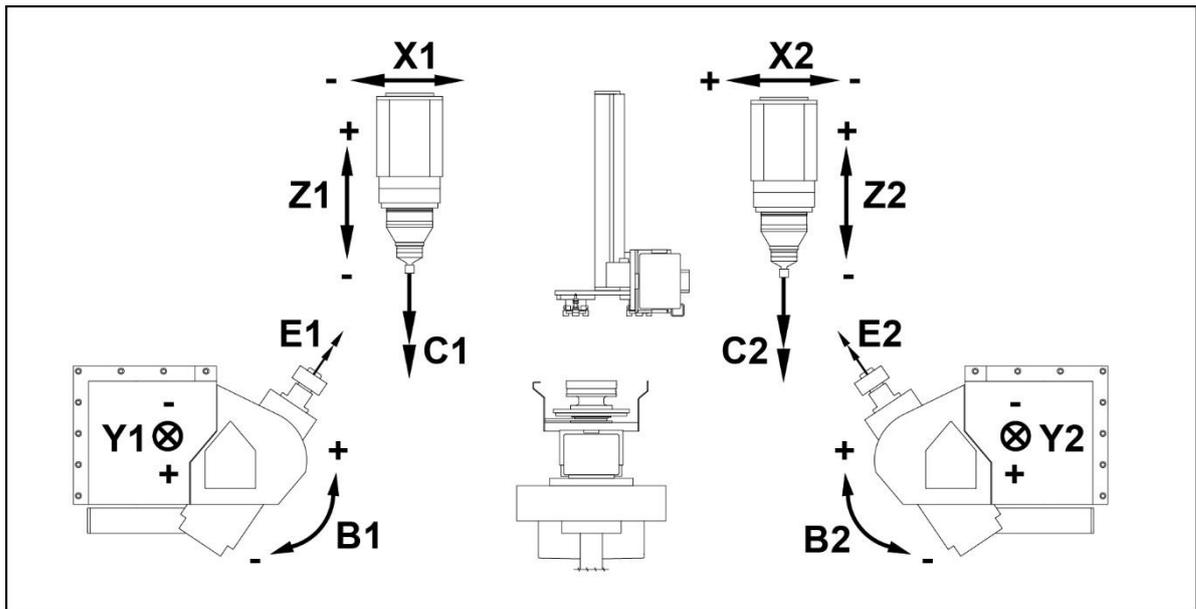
Achsen einer Doppelspindel Wälzschälmaschine SynchroForm
